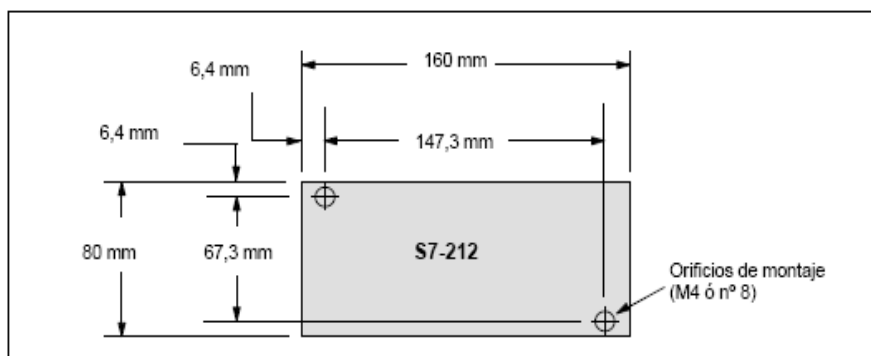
Dimensiones de montaje para un CPU S7-212.
